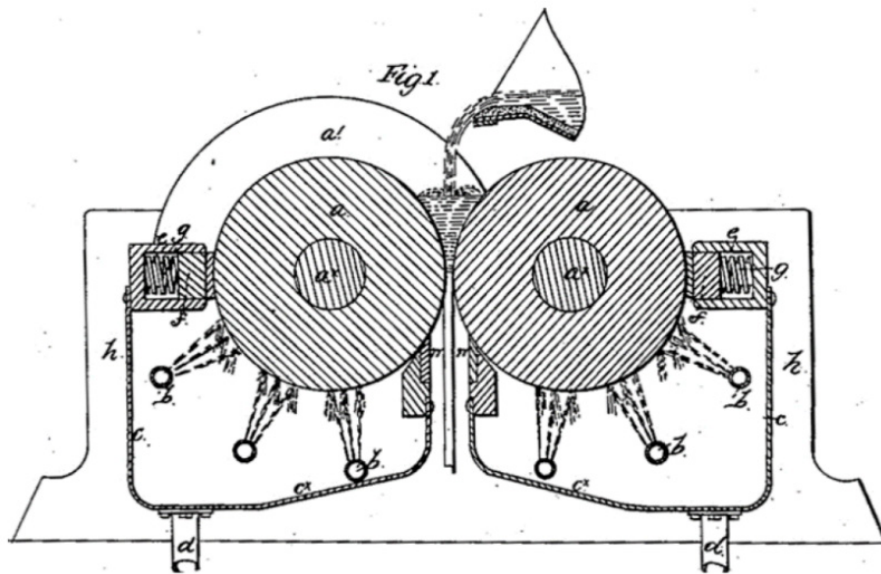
Ескіз машини валкової розливки-прокатки (1865 р.) [1]
